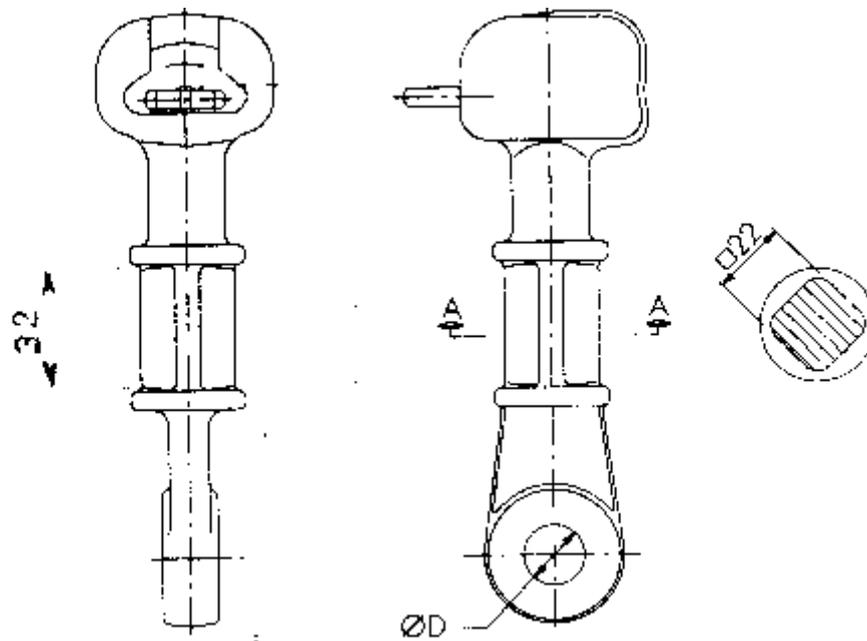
Geometria e dimensões da zona de fixação das hastes de guarda
